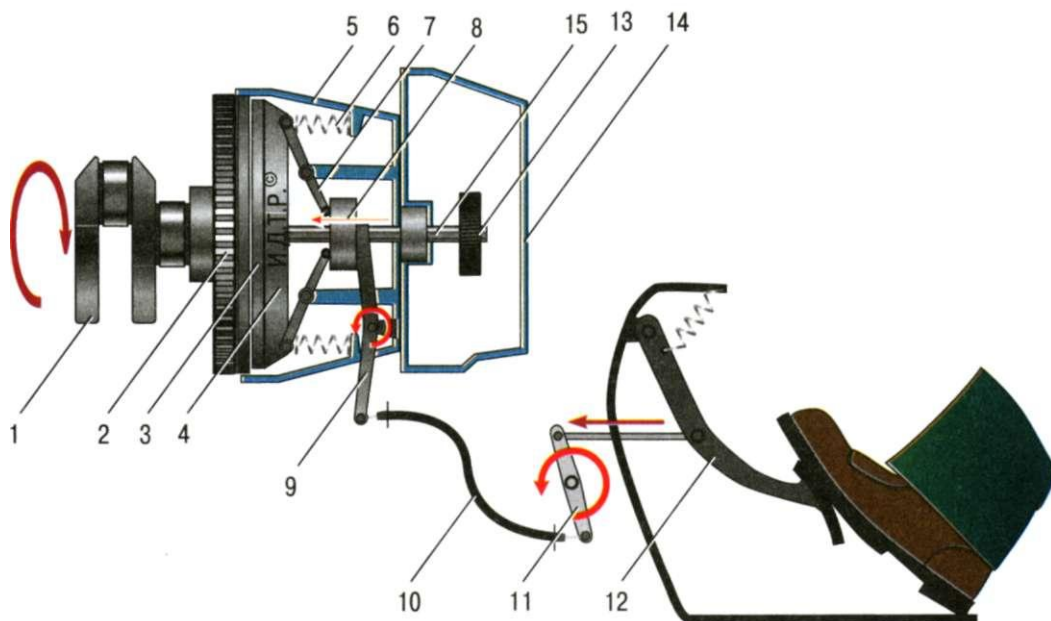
Схема механического привода выключения сцепления и механизма сцепления: 1 - коленчатый вал; 2 - маховик; 3 - ведомый диск; 4 - нажимной диск; 5 - кожух сцепления; 6 - нажимные пружины; 7 - отжимные рычаги;
